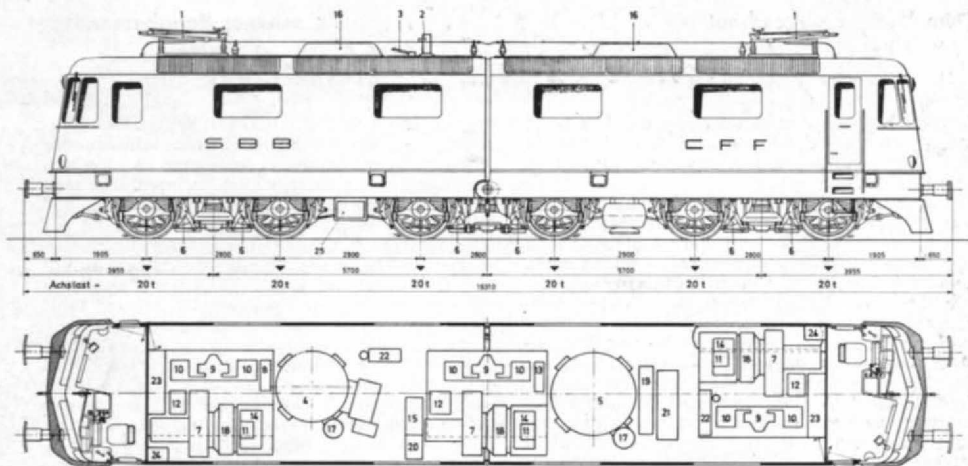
Typenskizze der geplanten SBB-Ellok 10 600 PS-Re 6/6 im N-Zeichnungsmaßstab 1:160, um N-Interessenten einen Anhalt zu geben; für die HO-Modellbauer gelten hauptsächlich die Angaben des Herrn Rothballer.
